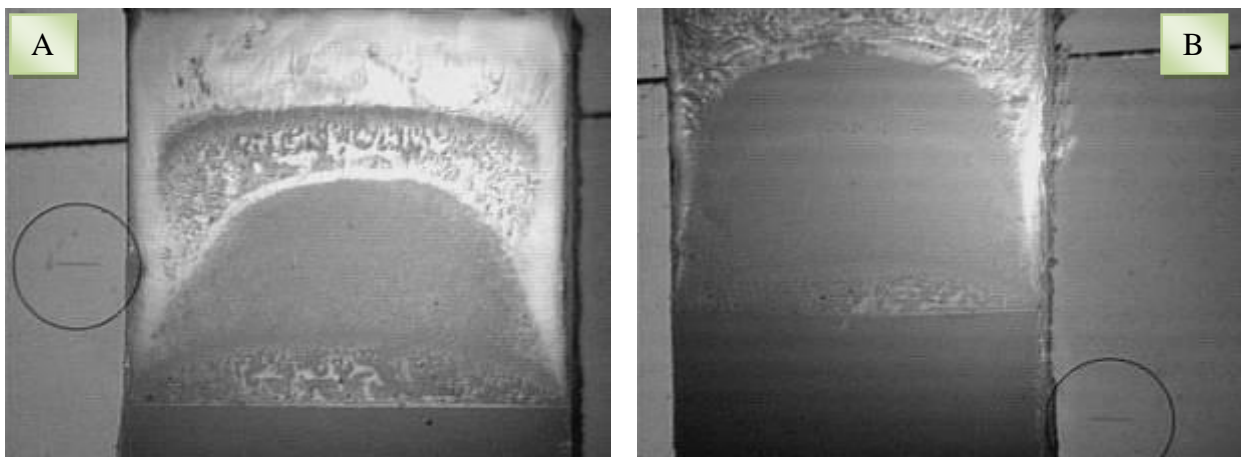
Superficie de fractura. A) HDPE; B) W-HDPE. Fractura ~ 20 °C.
